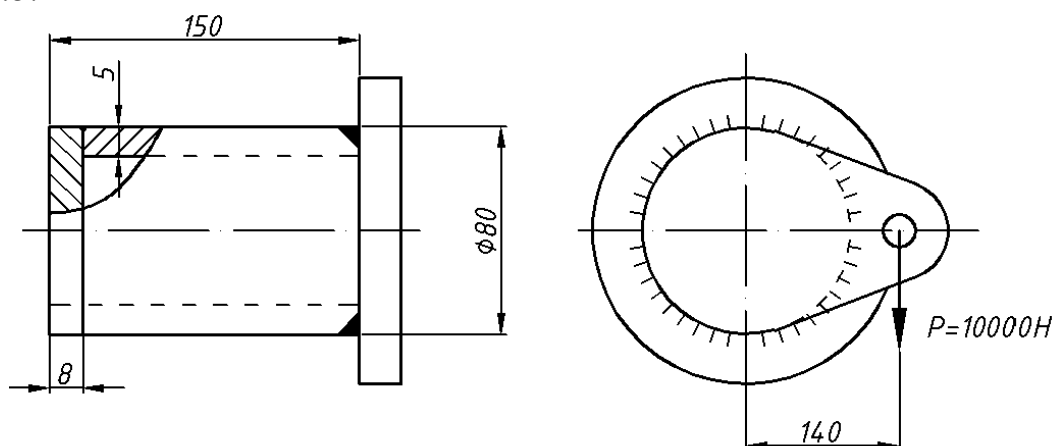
Сварное соединение кронштейна со стойкой
